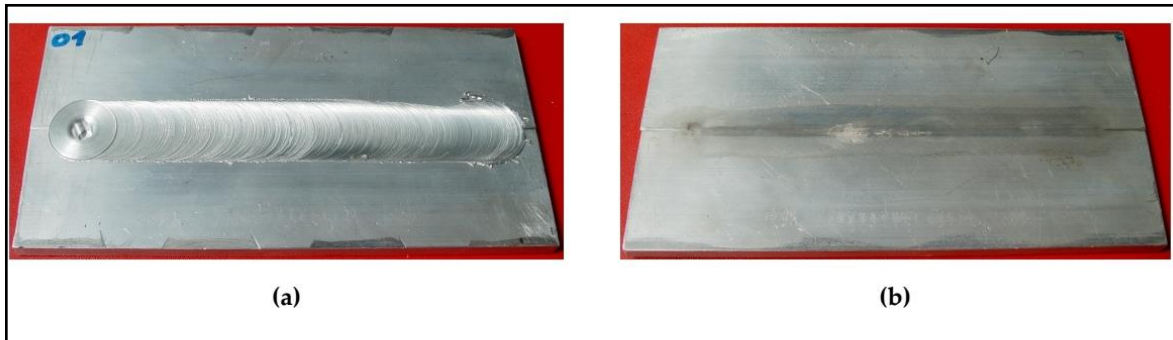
Le joint soudé au 1er point du plan expérimental. (a) Une vue du dessus ; (b) Une vue de dessous. [68]
